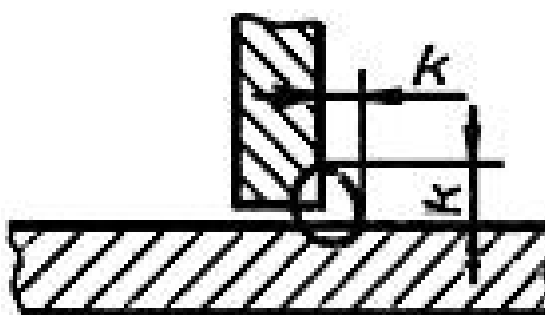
Конструктивные элементы сварного шва Т1
